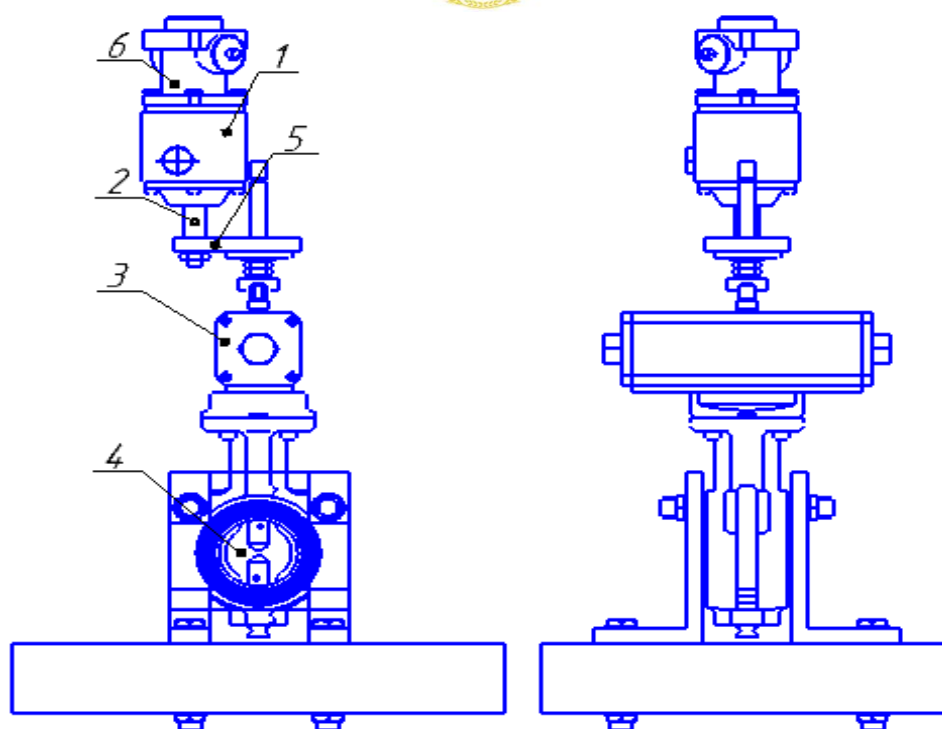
Общий вид автоматизированного привода задвижки: 1 — универсальный пневматический датчик; 2 — вал; 3 — поворотный цилиндр; 4 — дисковый затвор; 5 — зубчатая передача; 6 — фрикционный тормоз.
